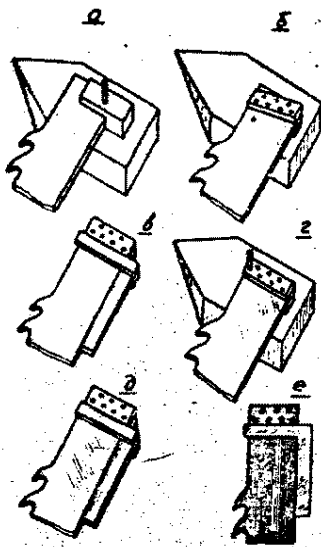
Последовательность операций при креплении планок к полотну рамной пилы: а – пробивка правого крайнего отверстия; б – крепление планок одной заклепкой; в – установка планок по угольнику; г – пробивка второго крайнего отверстия; д – проверка по угольнику перпендикулярности кромок планок задней кромке пилы; е – крепление планок на остальные заклепки и окончательный контроль.
